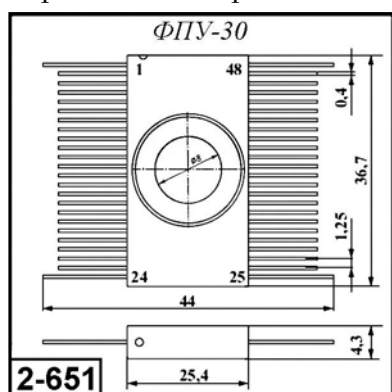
Внешний вид и габаритные размеры ФПУ-30
